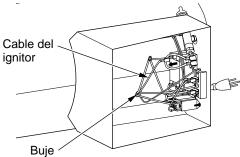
Desmontaje del cable del ignitor del transformador de chispa
